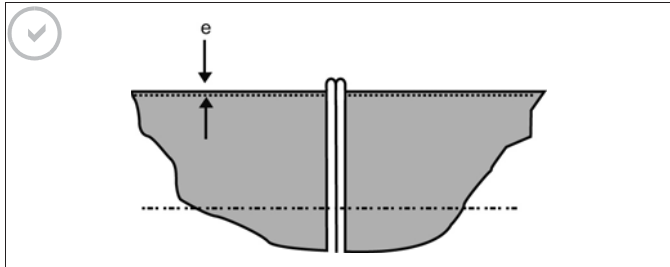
Сварка встык с равными наплавленными валиками (успешно)
